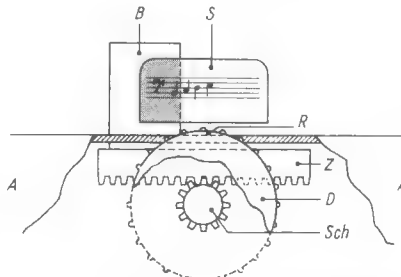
Draufsicht auf die Blendenmechanik der Klangeinsteller
